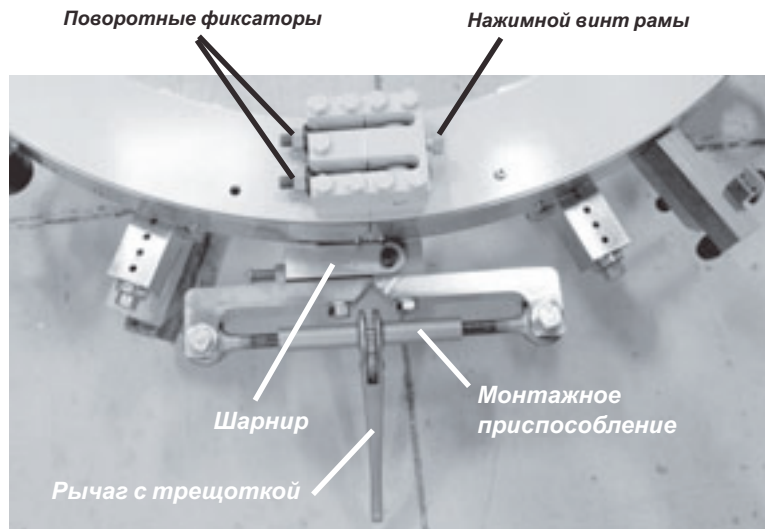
Установите шарнир и монтажное приспособление в точку разделения.
